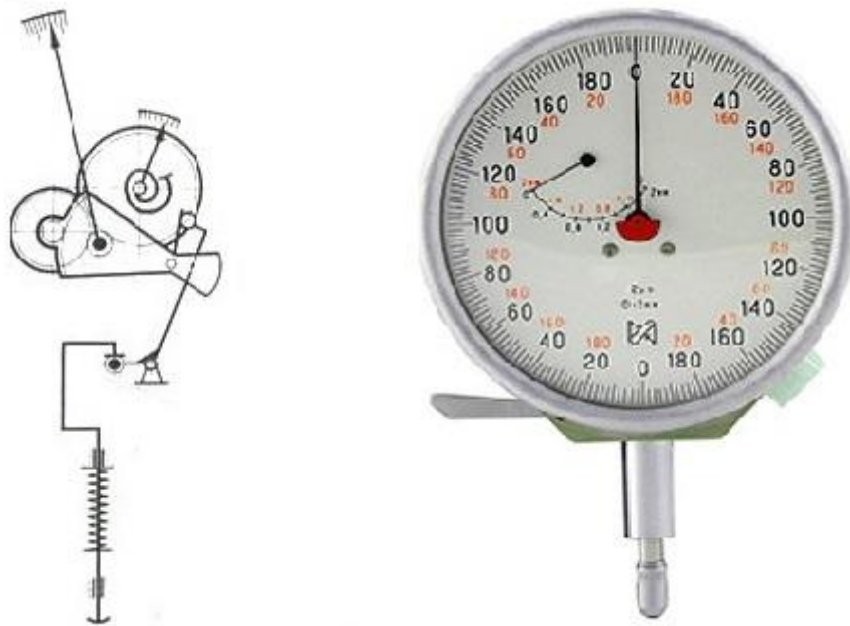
Многооборотный рычажно-зубчатый индикатор 2МИГ
